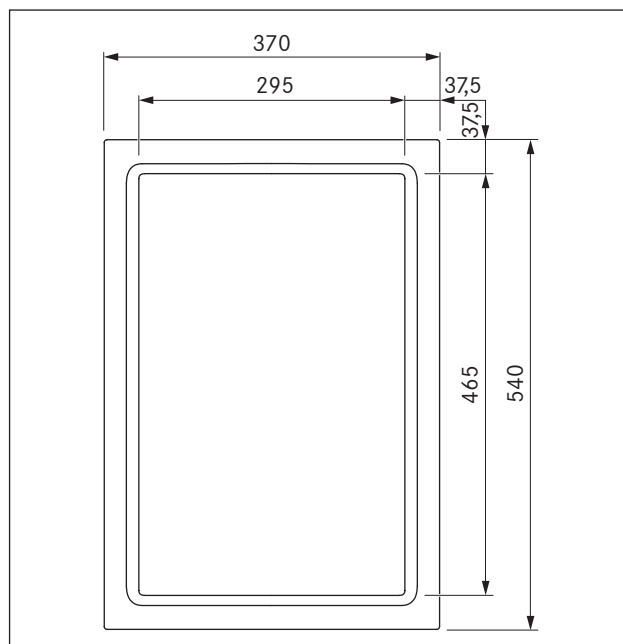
PKT11 dimensioni apparecchio vista da sopra
